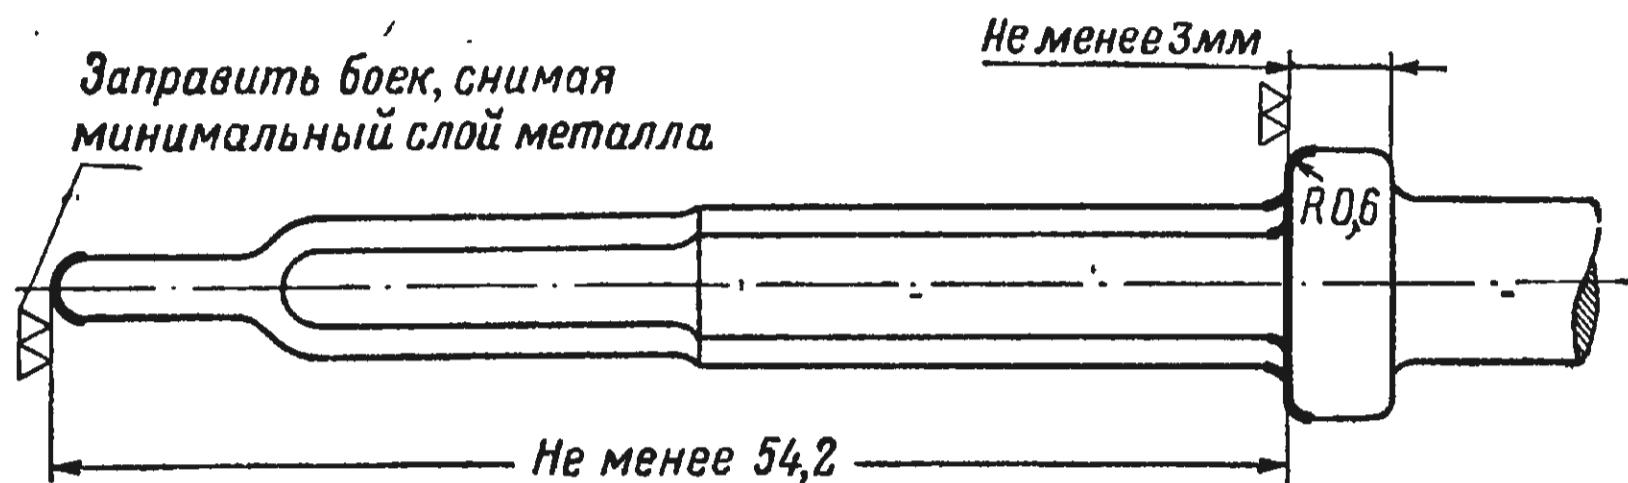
Оливка передней поверхности венчика ударника и заправка бойка
